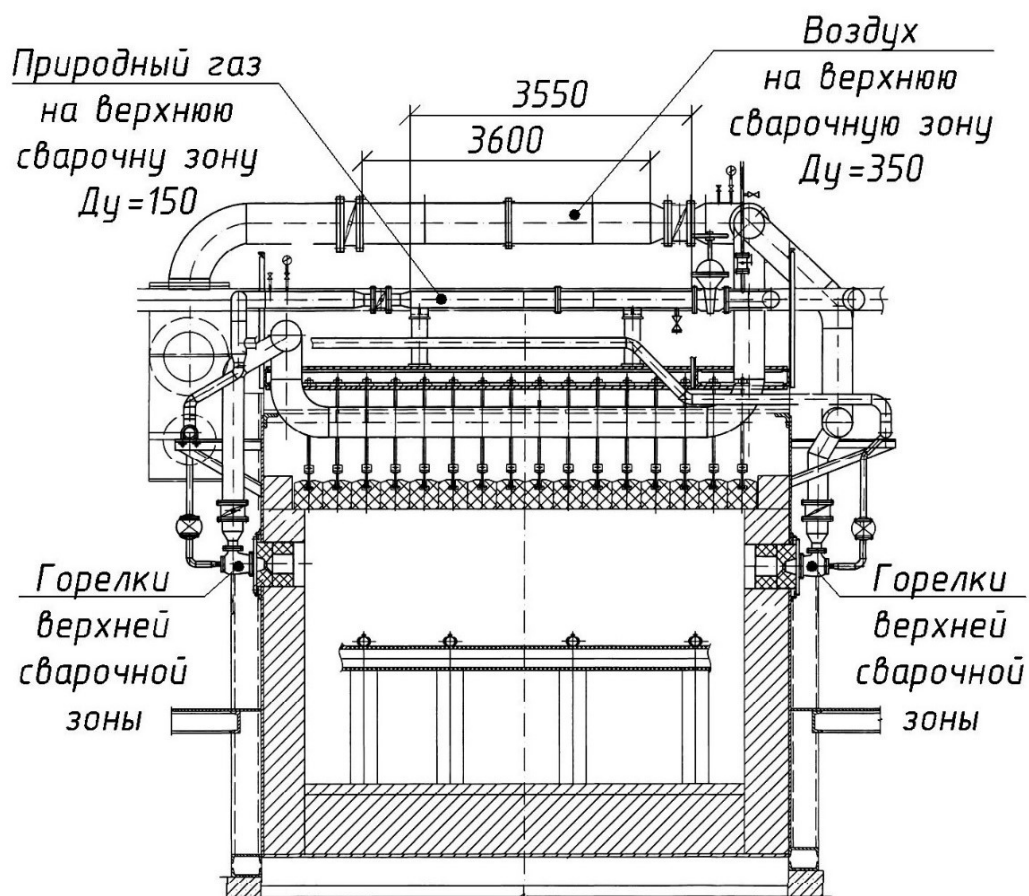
Поперечный разрез методической печи в верхней сварочной зоне
